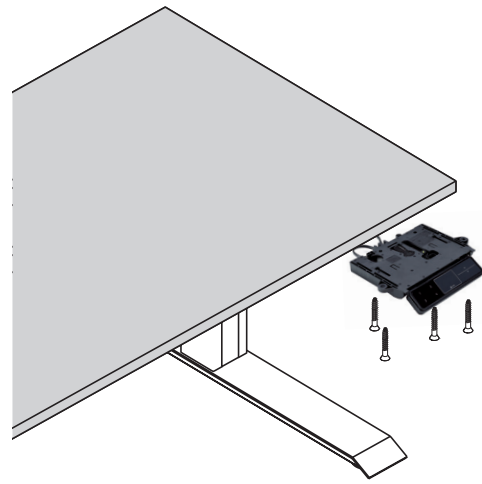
Handschalter LegaDrive Touch Comfort am Beispieltisch anbringen
